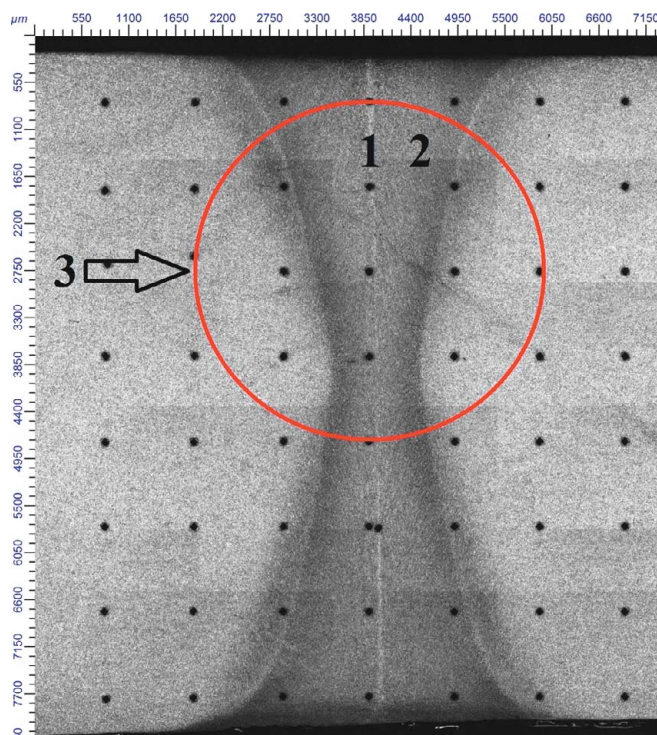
Схема вырезки dilatометрического образца (поперечное сечение) из сварного соединения трубы, сваренной ТВЧ: 1 — линия сплавления; 2 — зона термического влияния; 3 — dilatометрический образец
